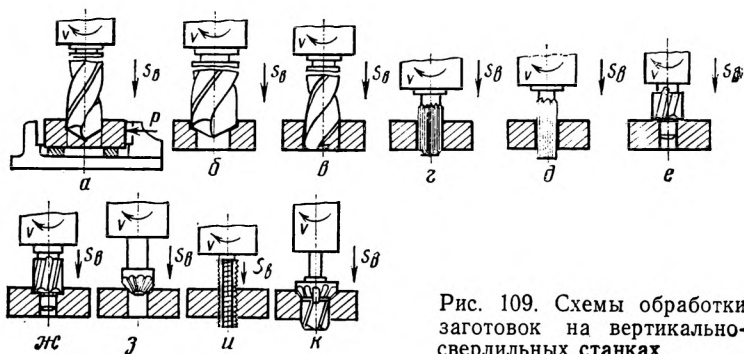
Схемы обработки заготовок на вертикально-сверлильных станках
